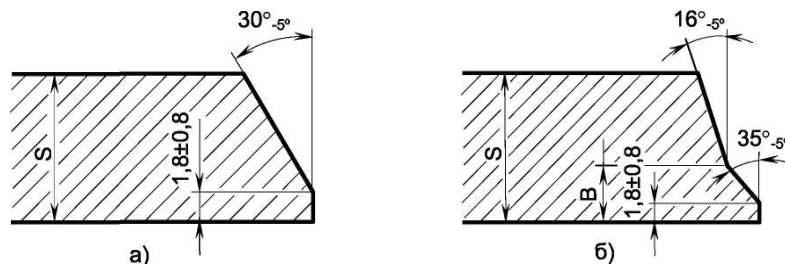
Форма разделки кромок труб для комбинированной сварки с применением Комплекса автоматической сварки
